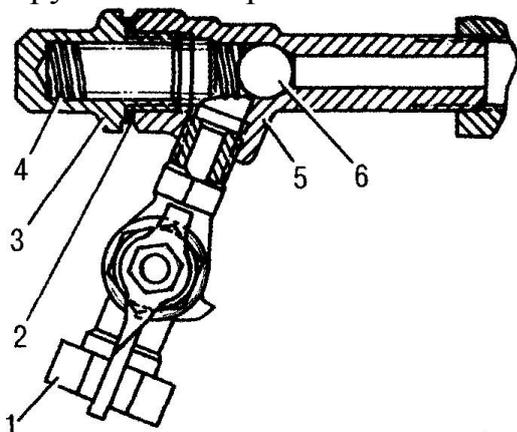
Предохранительный клапан и кран масляного радиатора: 1 - запорный краник; 2 - прокладка пробки клапана; 3 - пробка клапана; 4 - пружина клапана; 5 - корпус клапана; 6 - шарик клапана
